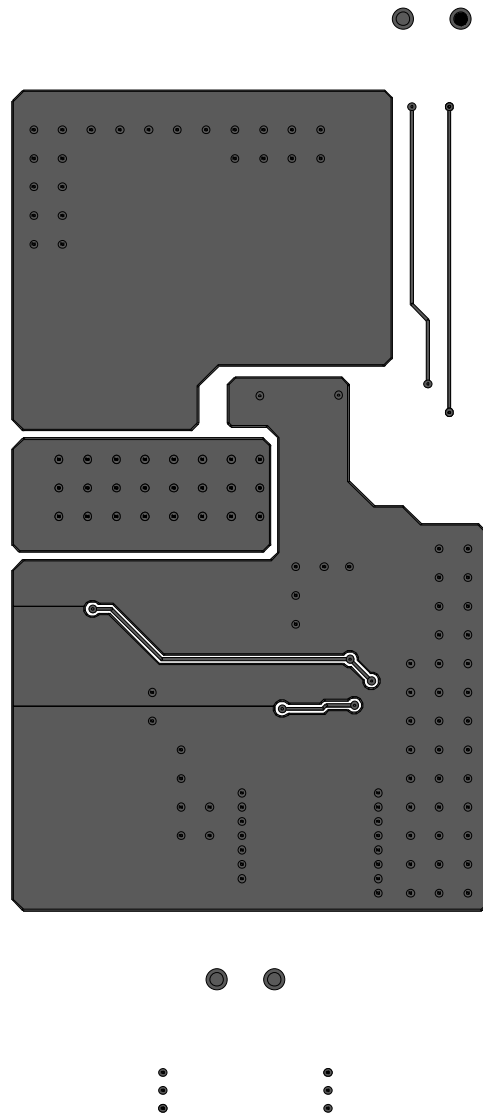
+7,3V-omvandlare lager 3 helt jordplan
